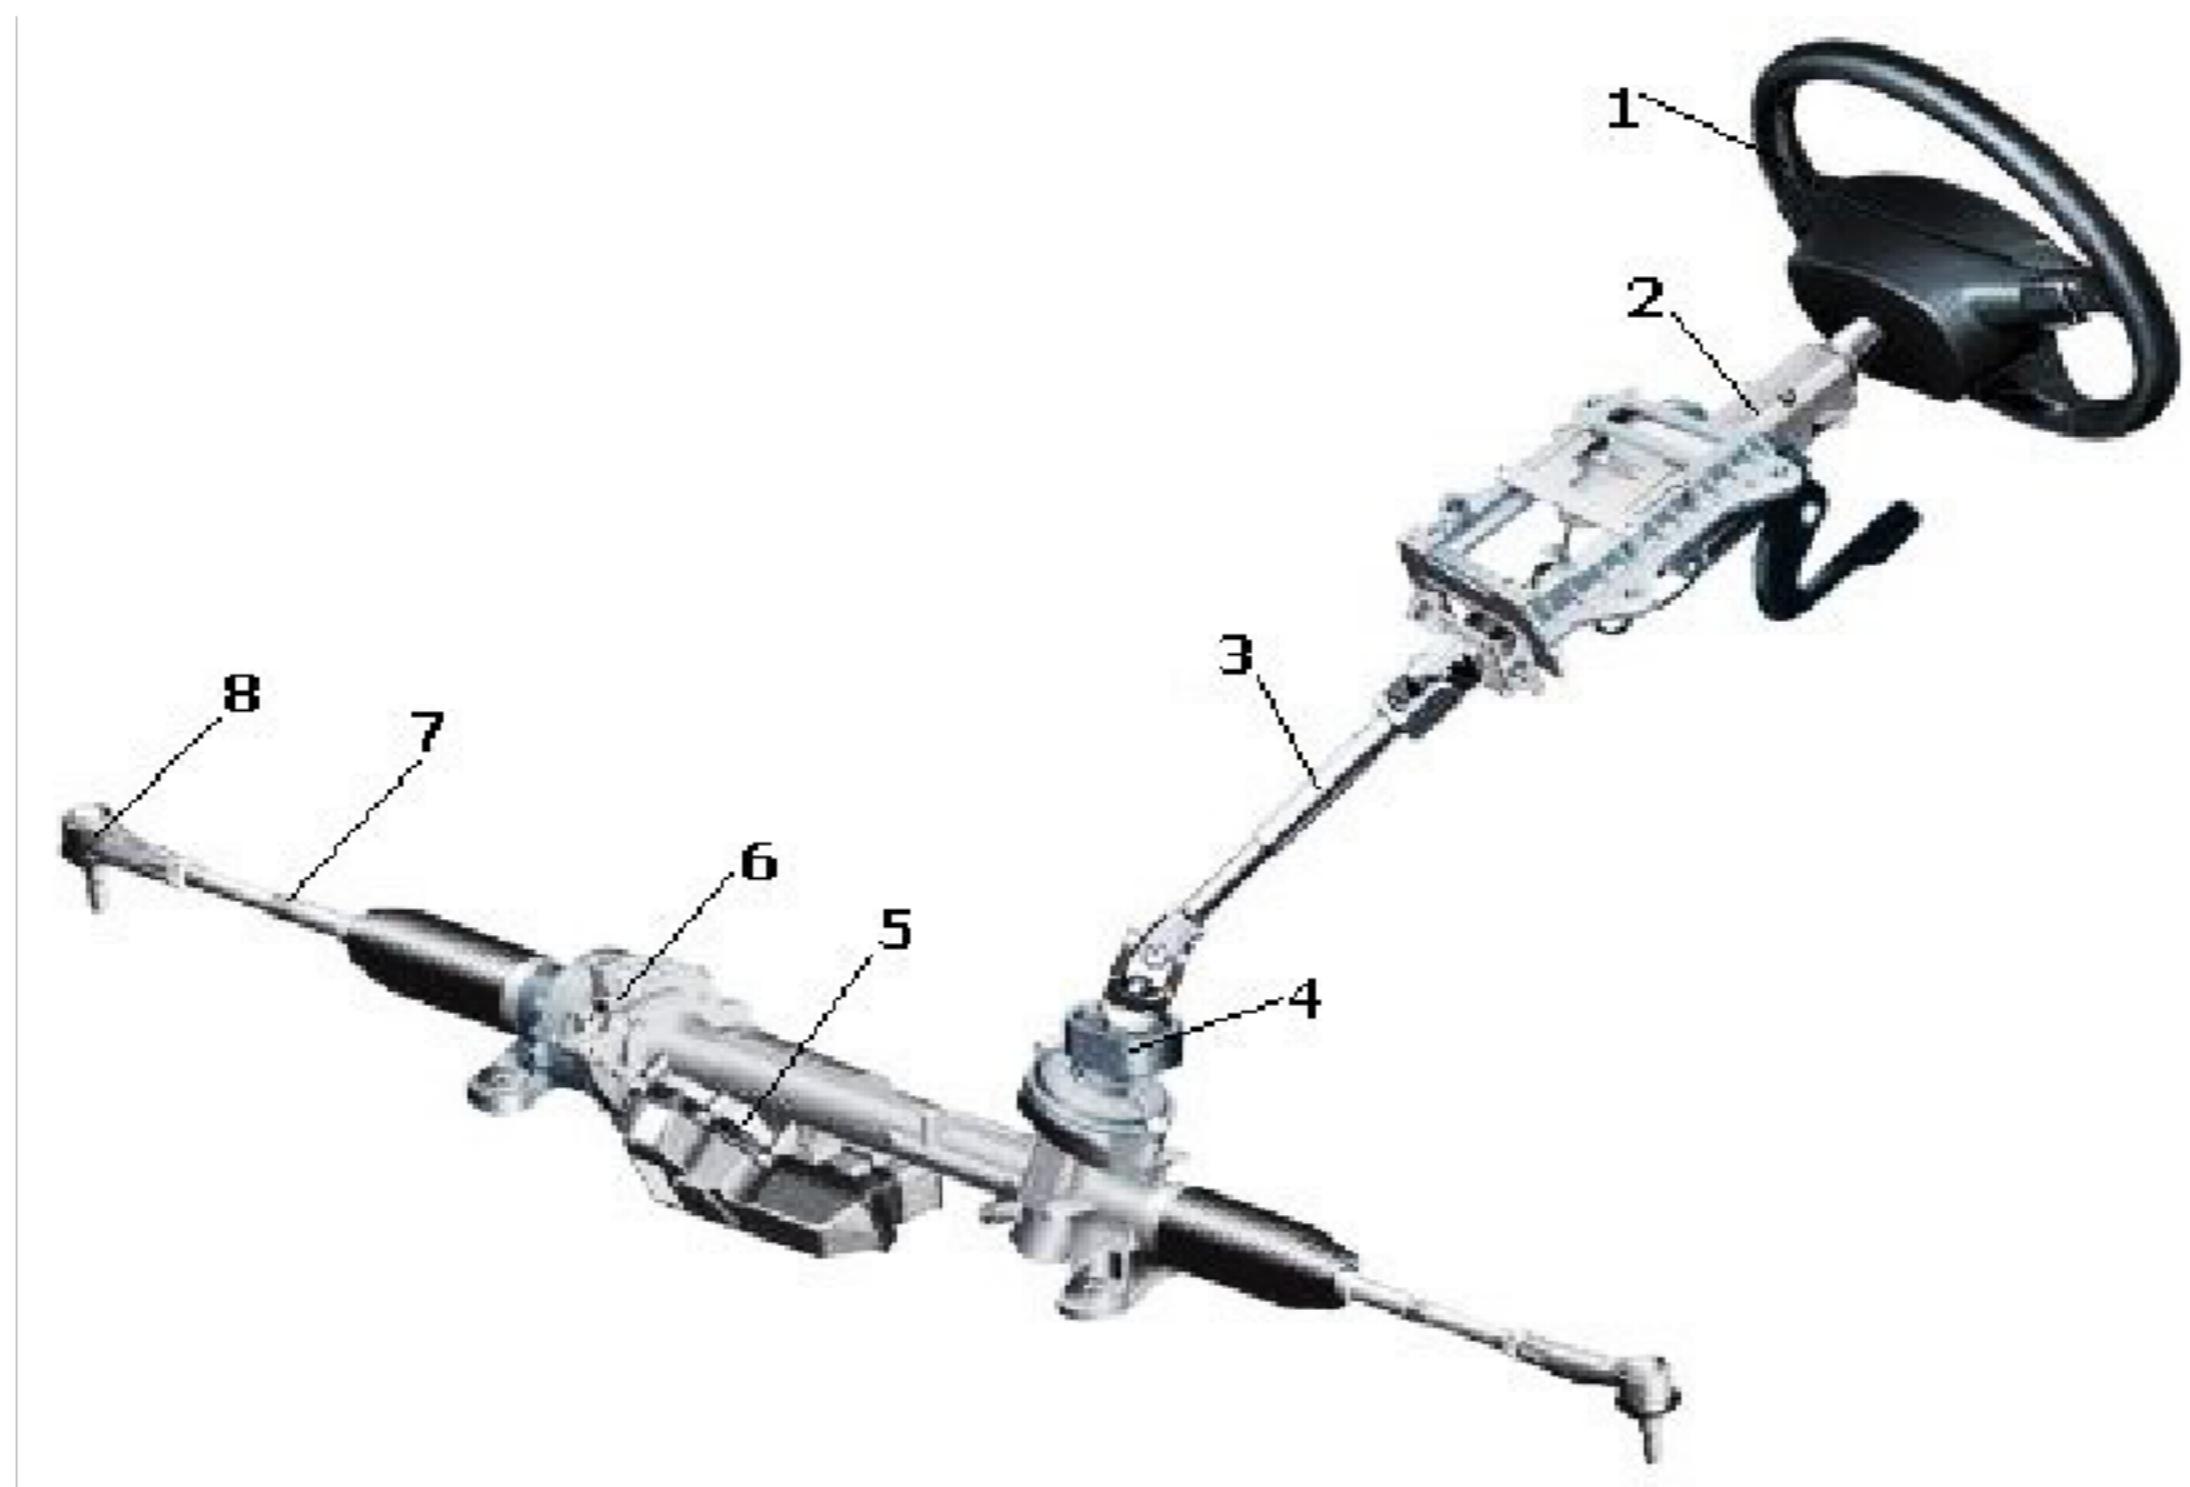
Общий вид рулевой механизма типа шестерня-рейка: 1 - рулевое колесо; 2 - рулевая колонка; 3 - карданный вал; 4 - датчик или золотниковое устройство крутящего момента на рулевом колесе; 5 - электроусилитель или гидроусилитель руля; 6 - рулевой механизм; 7 - рулевая тяга; 8 - наконечник рулевой тяги с шаровым шарниром.
